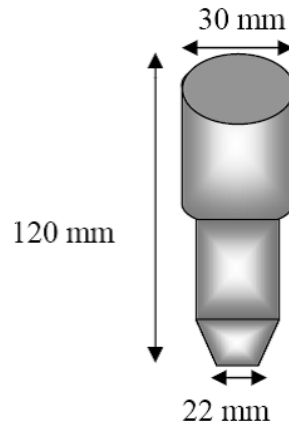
Moule utilisé pour le découpage des éprouvettes (poinçon).
